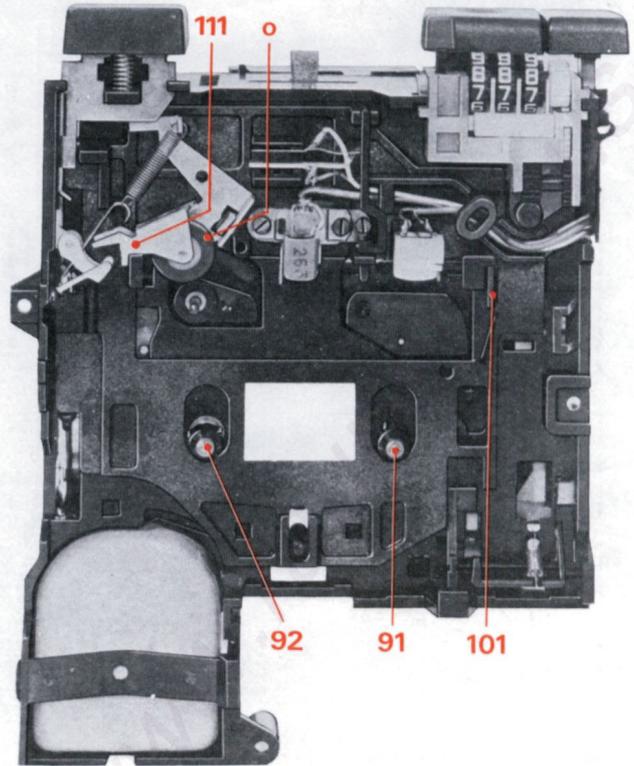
Andruckrolle, Kupplungen und Wickelteller
